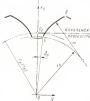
Параметры профиля эвольвентного зубчатого колеса
